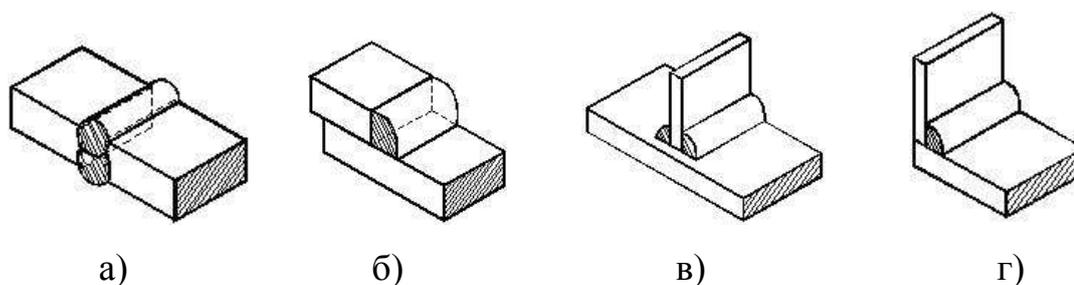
Сварные соединения: а - стыковое; б - внахлестку; в - тавровое; г - угловое.
